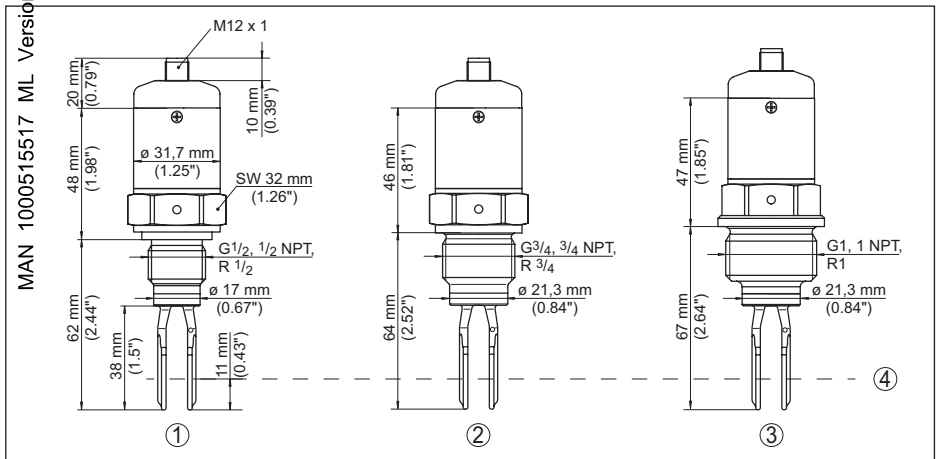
LEVEL SWITCH 8110, Standardausführung - Gewindeanschlüsse
